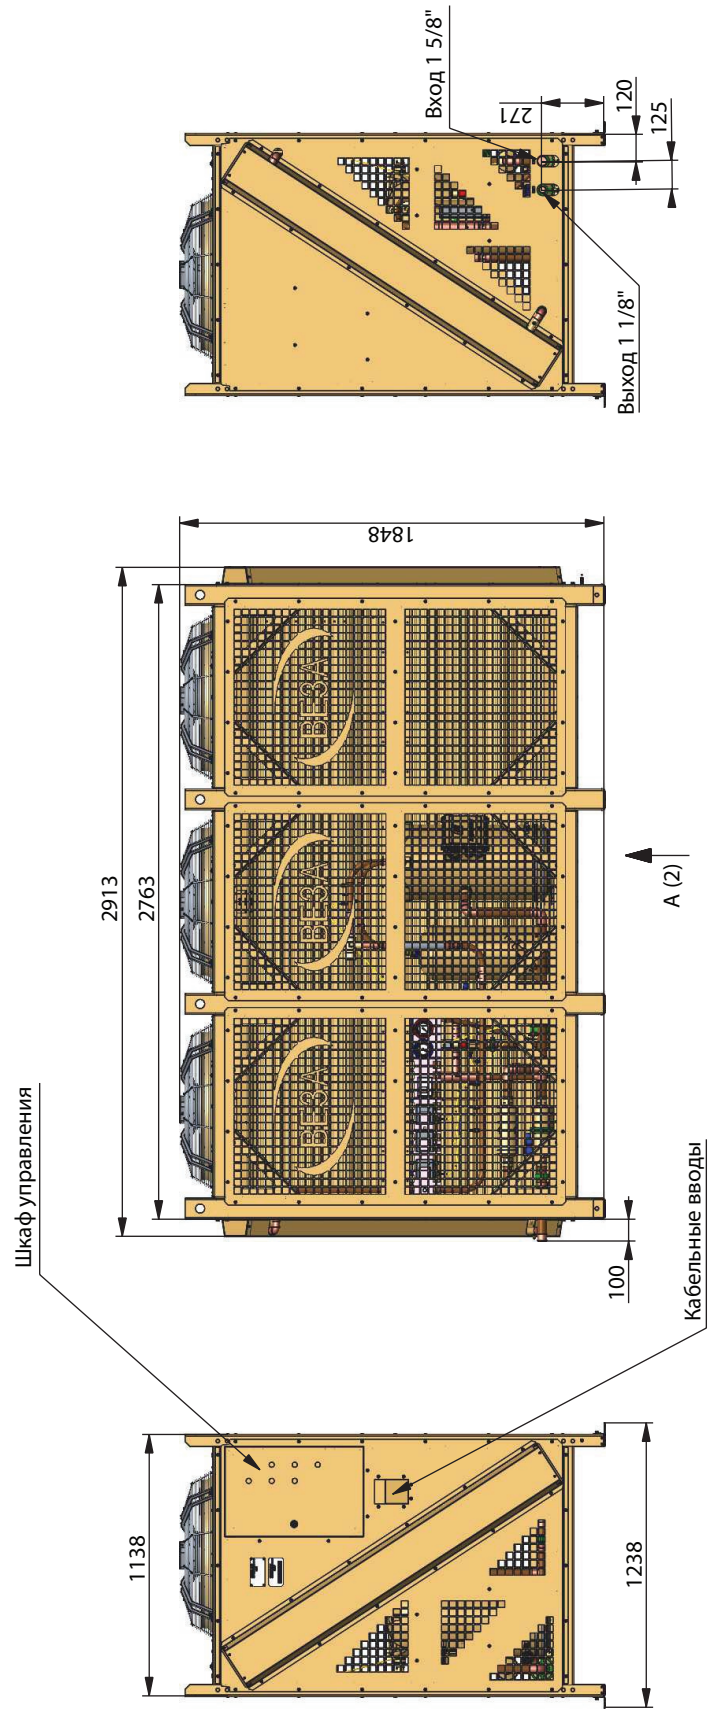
Агрегат компрессорный МАКК 120-951
